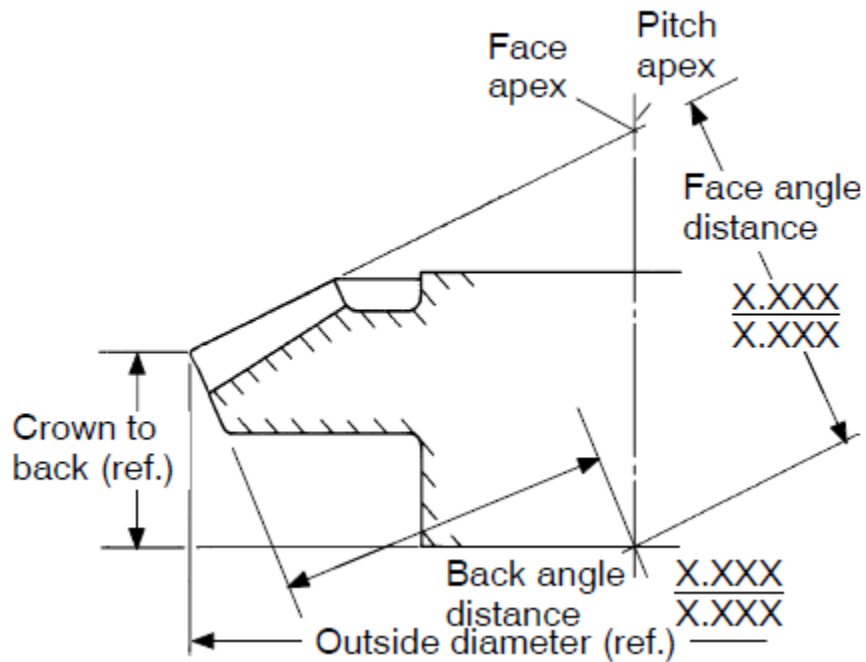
Método 1, para especificar las tolerancias en engranajes cónicos.
